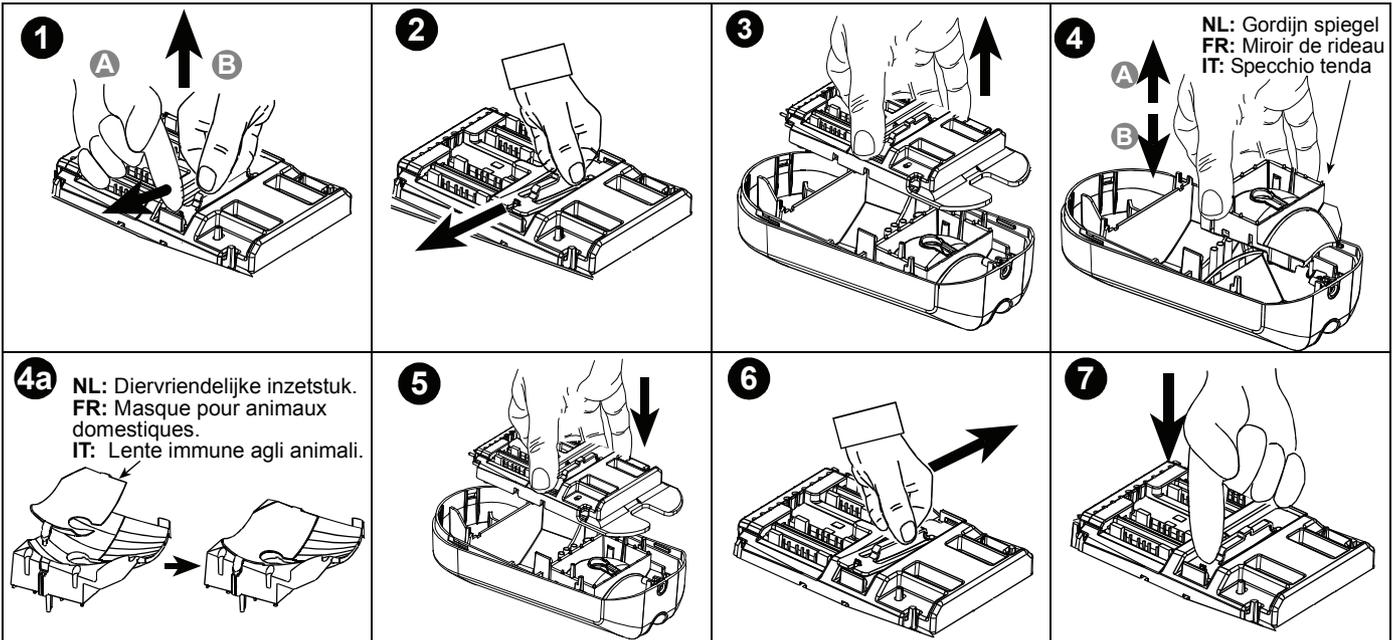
TOWER-10 AM Long Beam Spiegel en diervriendelijk inztels / Remplacement du miroir longue portée et du masque pour animaux domestiques sur le TOWER 10 AM / TOWER 10 AM Sostituzione lente a lunga portata e lente immune agli animali
